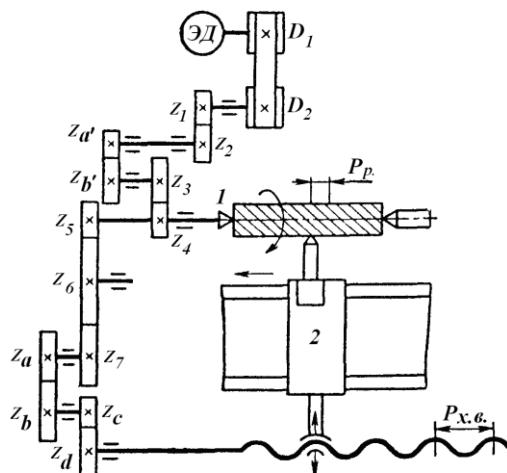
Упрощенная кинематическая схема условного токарно-винторезного станка
